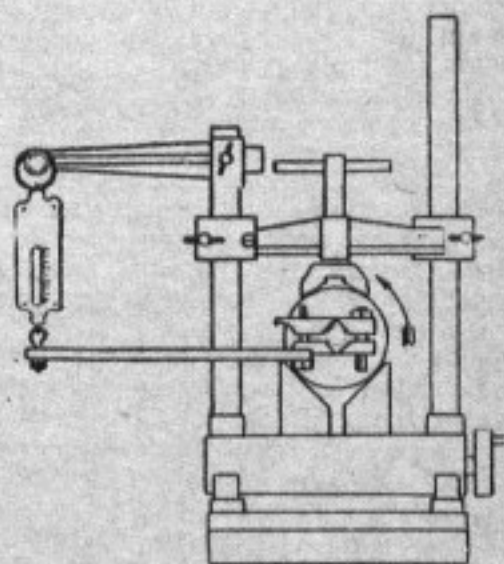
Установка стартера для проведения контрольного испытания на стенде
